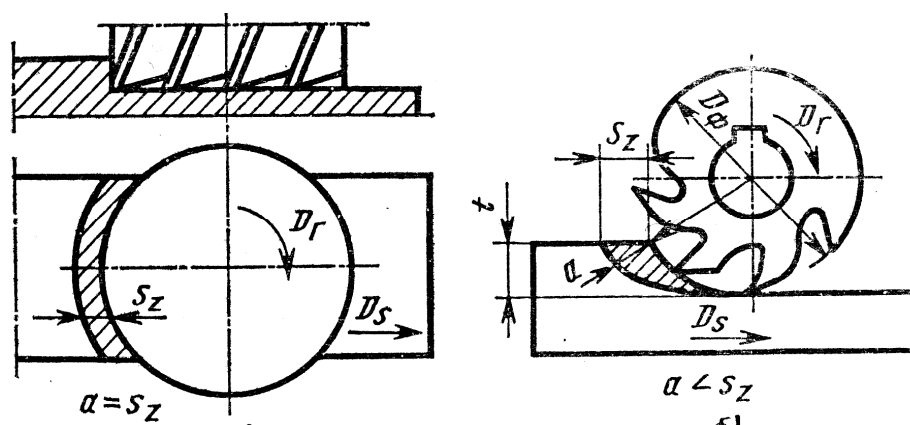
Толщина стружки при торцовом (а) и цилиндрическом (б) фрезеровании
